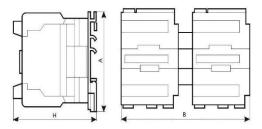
Контактор реверсивный ПМЛ-5560М
